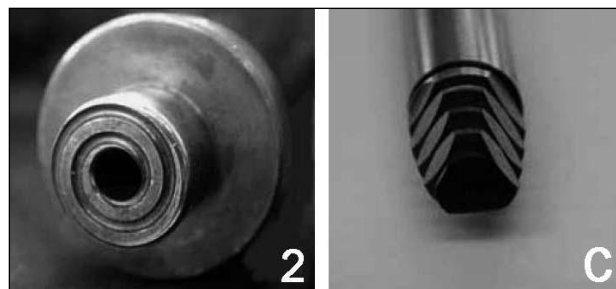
Shoulder* e pino usados na soldagem das chapas.
